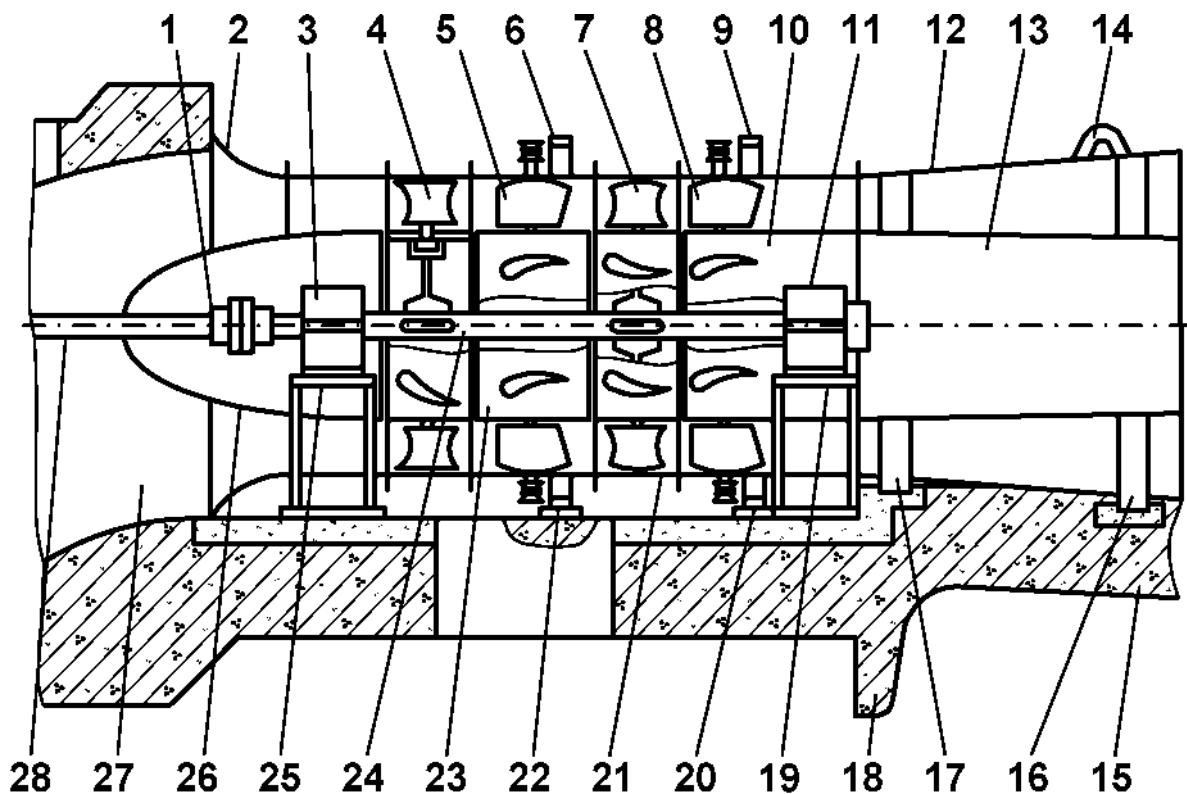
Продольное сечение вентилятора ВОД-40М:
